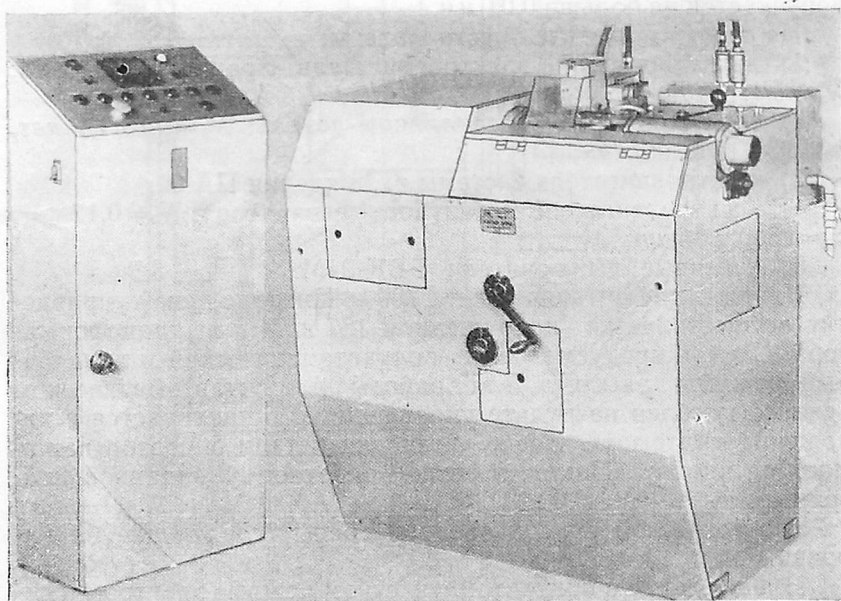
Общий вид станка мод. МАС-3 для обработки золотников
